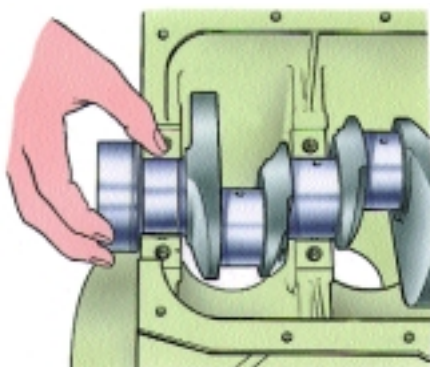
Установка упорных полуколец на задней опоре двигателя мод. 2106–70
